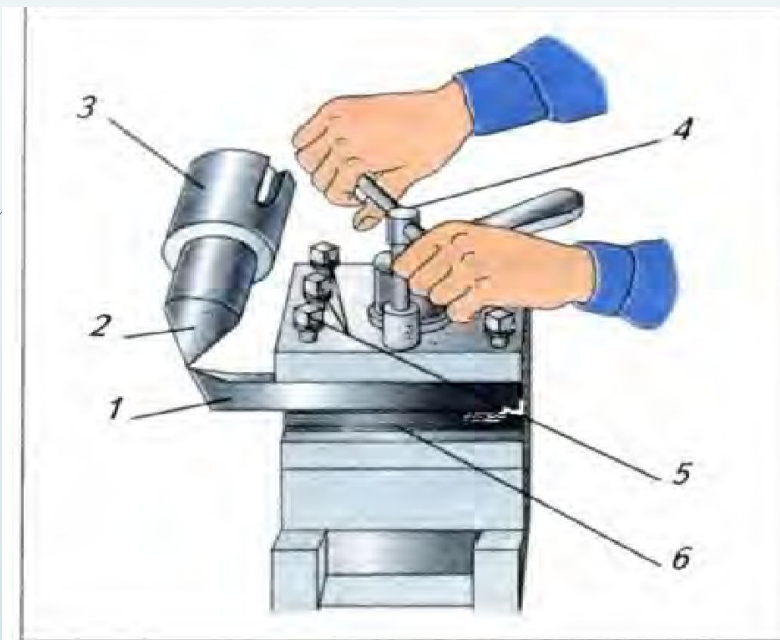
Установка токарного резца в резцедержателе: 1 — резец; 2 — задний центр; 3 — пиноль задней бабки; 4 — ключ; 5 — винты крепления резца; 6 — подкладка под резец
